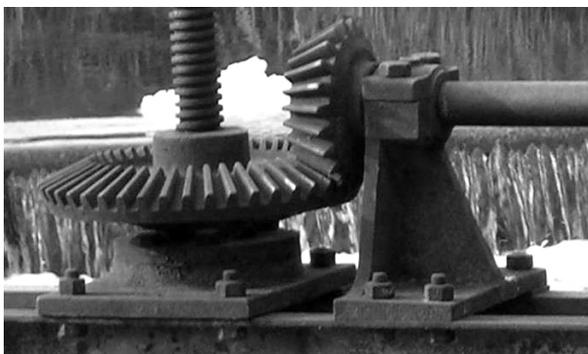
| Sistema de transmissão mecânico com polias e engrenagens
